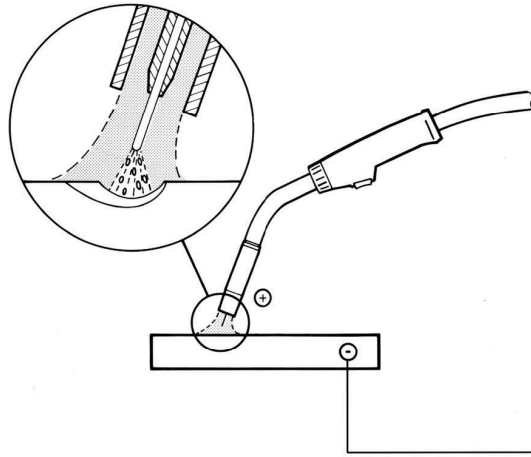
Schéma de principe du soudage MIG/MAG.
